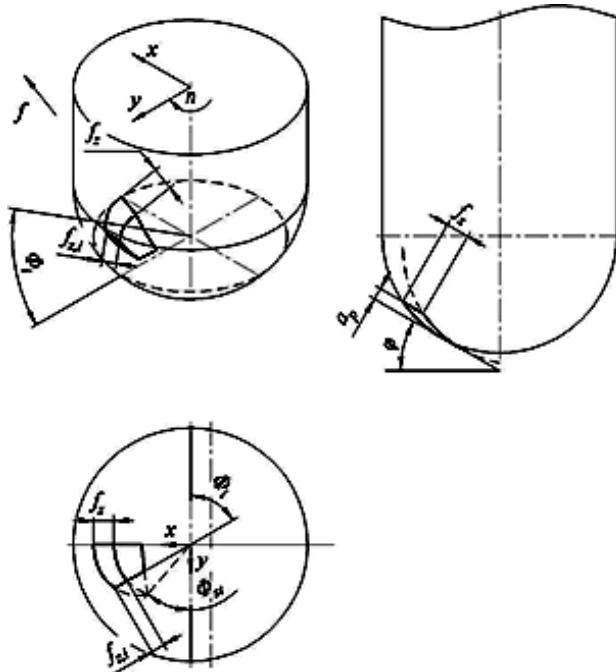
Схема обробки радіусною фрезою похилої поверхні
